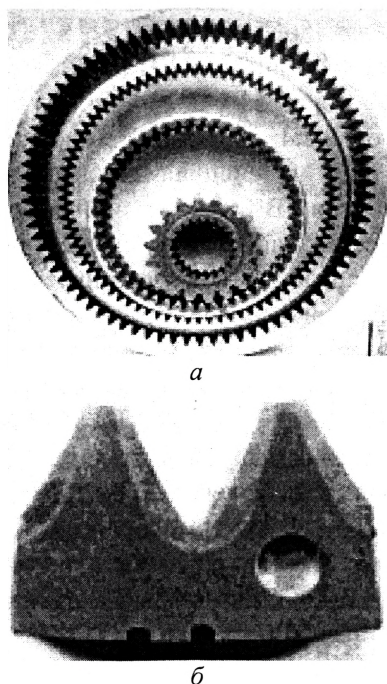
Индукционная закалка шестерен: а — шестерни, подвергаемые поверхностной индукционной закалке, б — зона закалки на зубчатой поверхности ведомой шестерни колесной передачи автомобиля МАЗ
